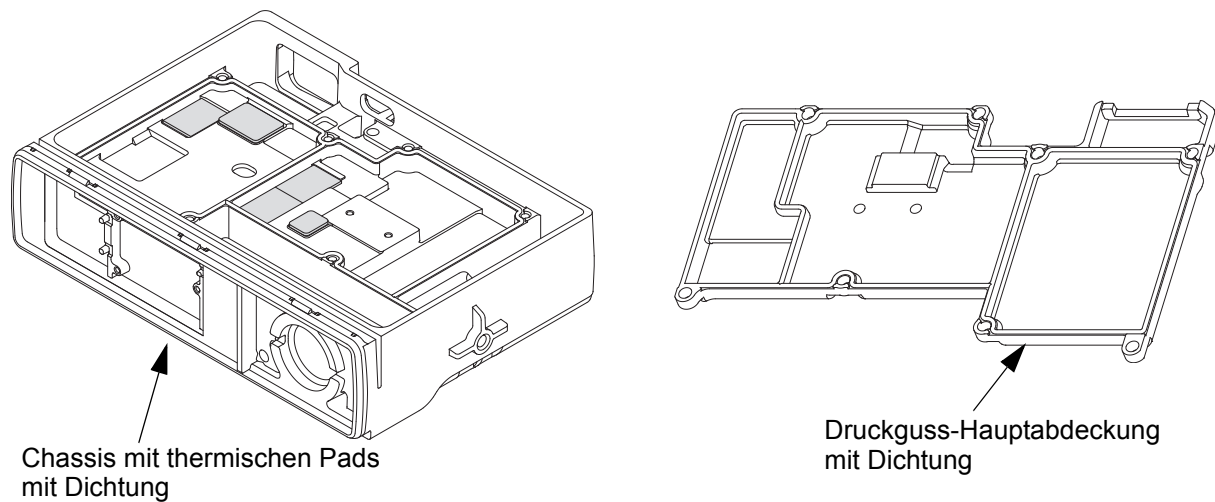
Thermische Pads und Dichtung auf Chassis und Druckguss-Hauptabdeckung
